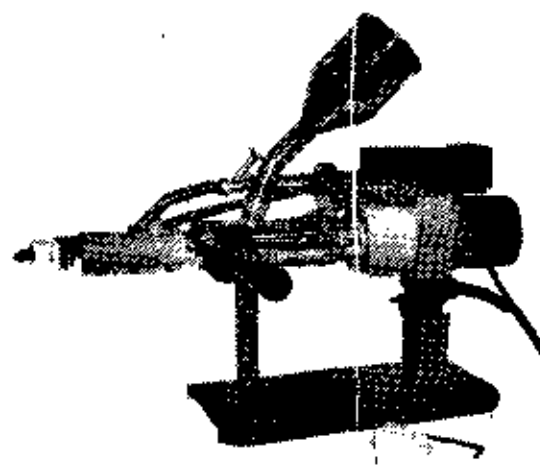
Ручной шнековый экструдер для экструзионной сварки
